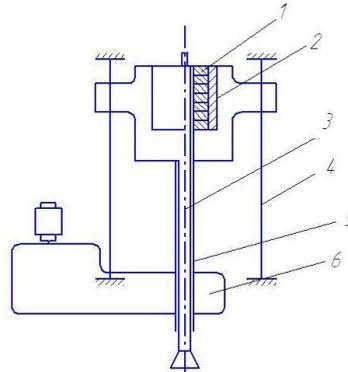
Кинематическая схема адаптивного вращательно-подающего механизма бурового станка с непосредственной электромагнитной подачей рабочего органа: 1 – обмотка линейного двигателя, 2 – линейный трехфазный асинхронный двигатель, 3 – штанга, 4 – стойка крепления механизма подачи, 5 – пустотелый шпиндель, 6 - вращатель (редуктор)
